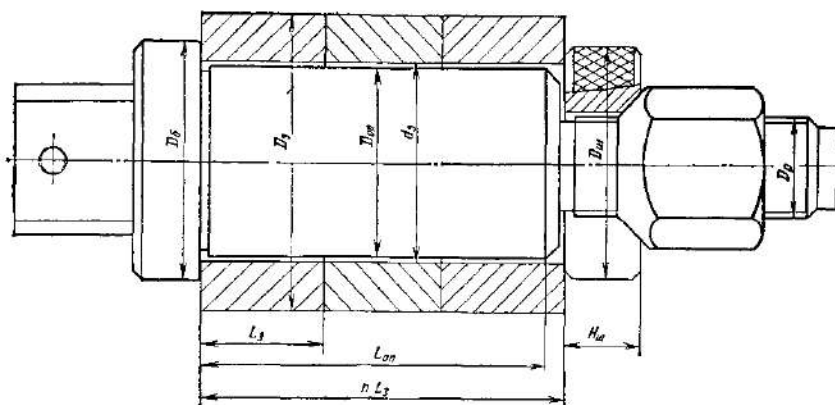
Цилиндрическая оправка для установки заготовок с гарантированным зазором
